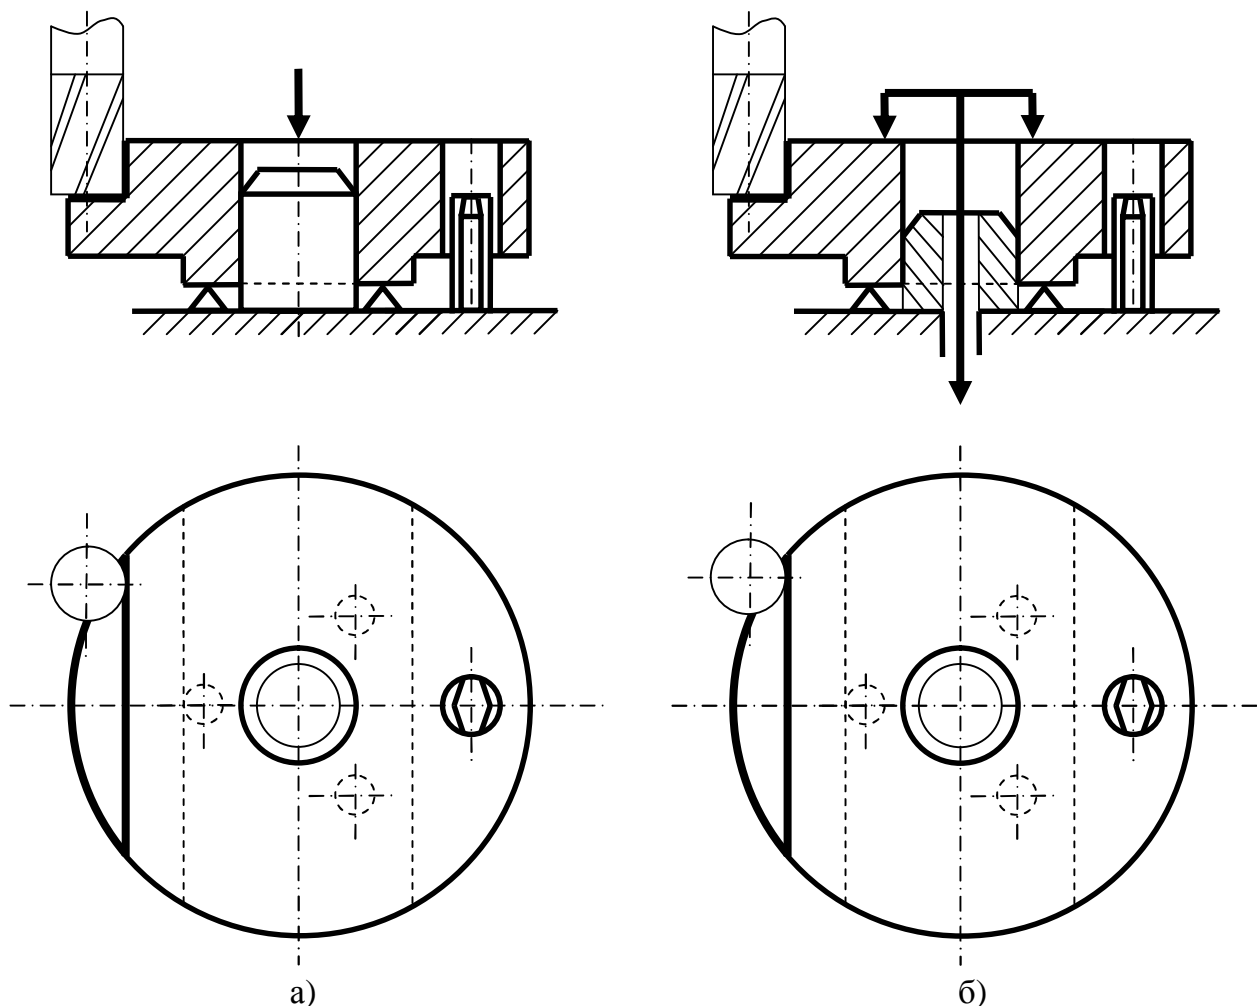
Схемы установки, реализующие предложенную схему базирования
